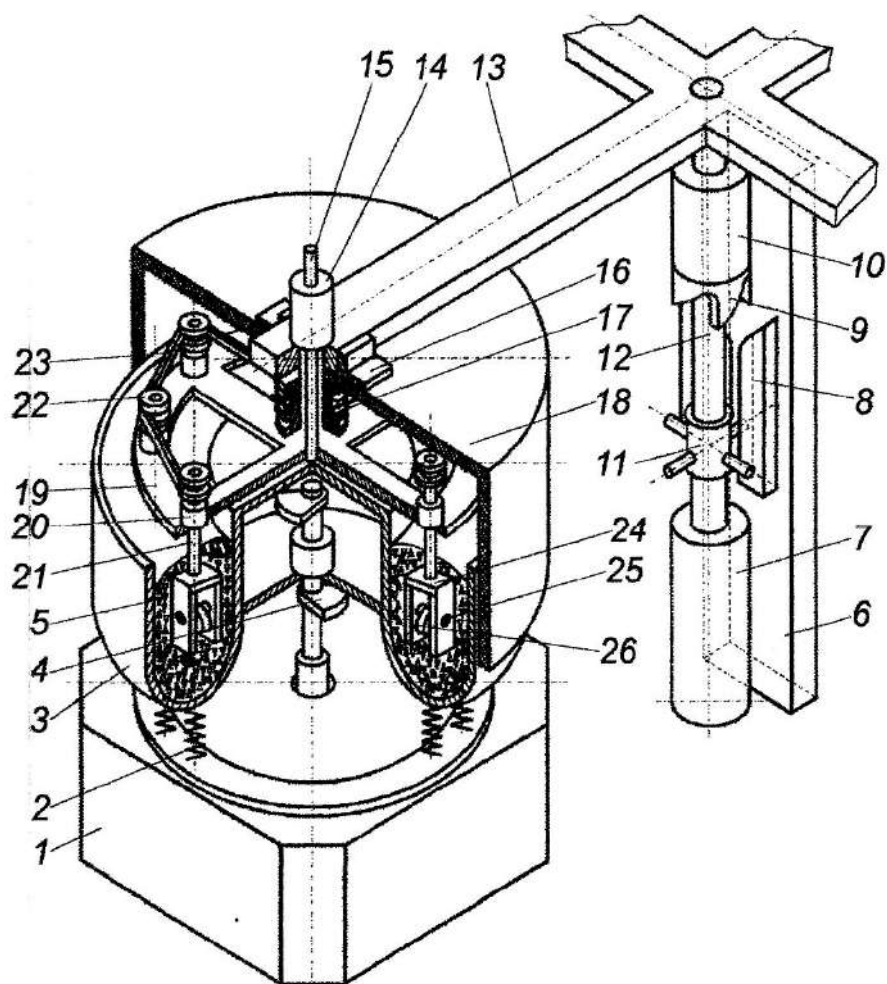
Пристрій для вібраційної шпиндельно-планетарної обробки деталей
